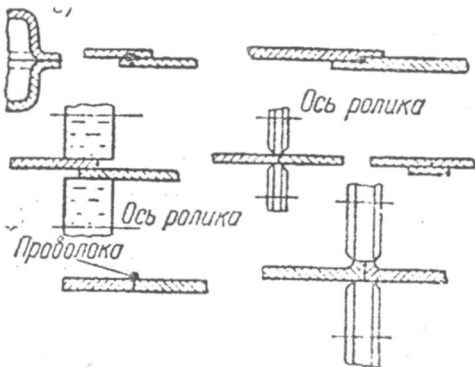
Типы изделий, получаемых шовной сваркой
